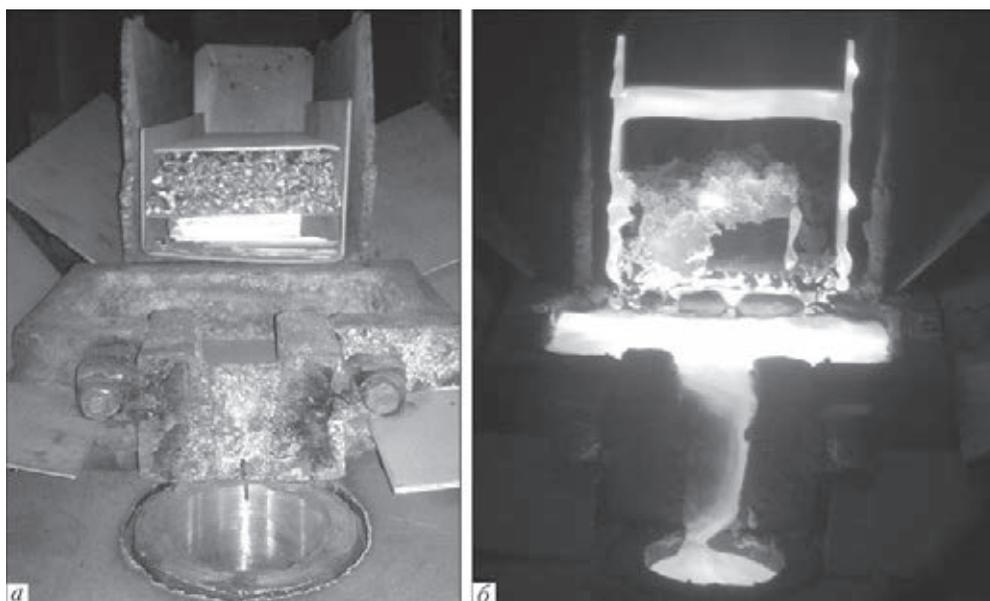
Исходная шихтовая заготовка (а) и процесс ее плавки (б) для получения интерметаллида Ti_2AlNb
